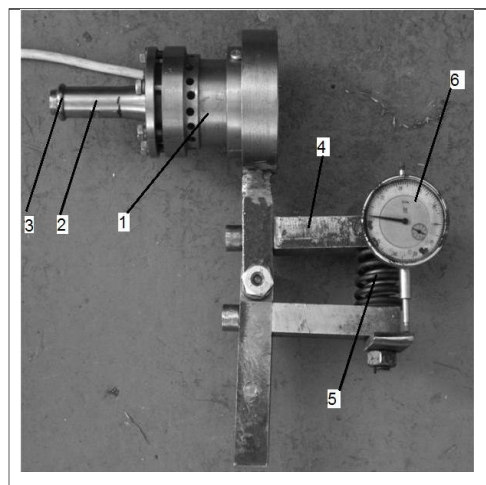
Стенд для ультразвукової обробки металу:
